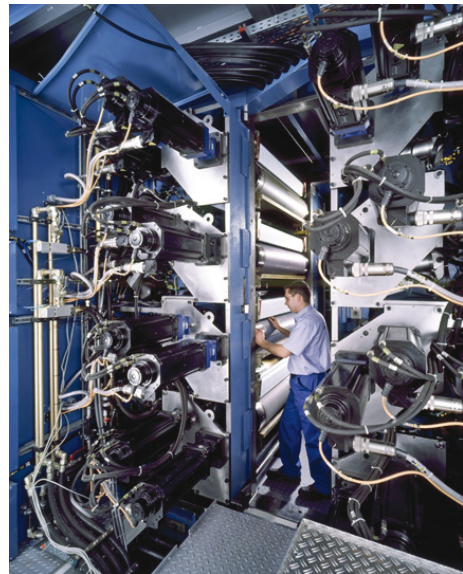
Druckmaschinen (© Koenig & Bauer AG)
